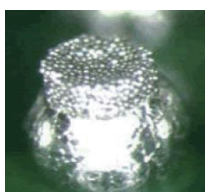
将焊锡膏印刷到 BGA 焊球上的状态
